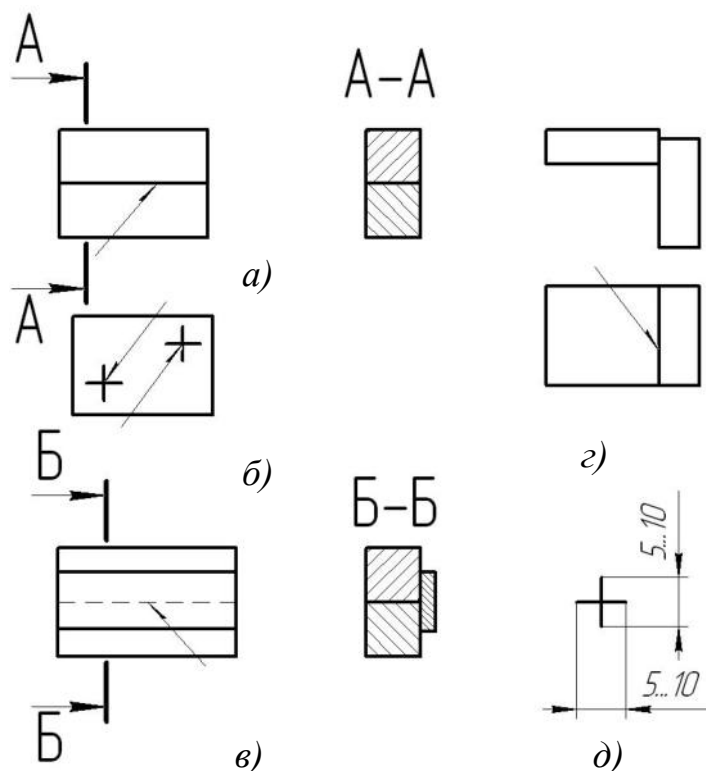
Условное изображение видимых и не видимых сварных швов сварных соединений
